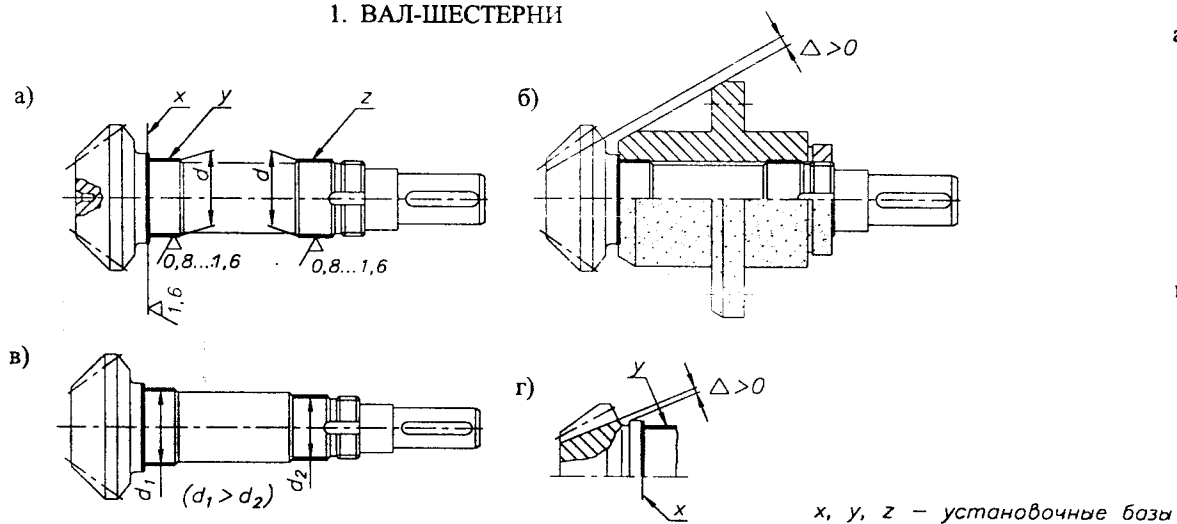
Установочные базы для нарезания зубьев на вал-шестернях
